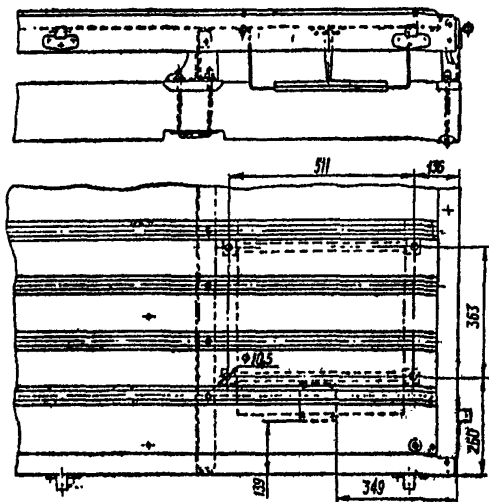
Установка инструментального ящика на автомобиле ГАЗ-53-07 и ГАЗ-52-08
